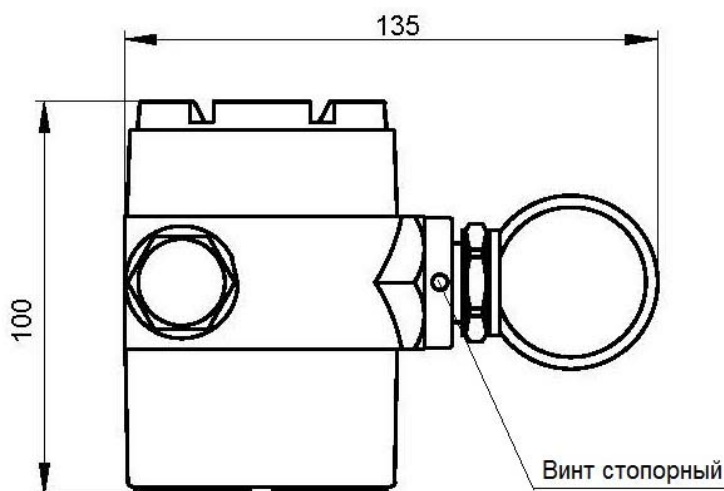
Преобразователь – вид сверху (показан условно).
